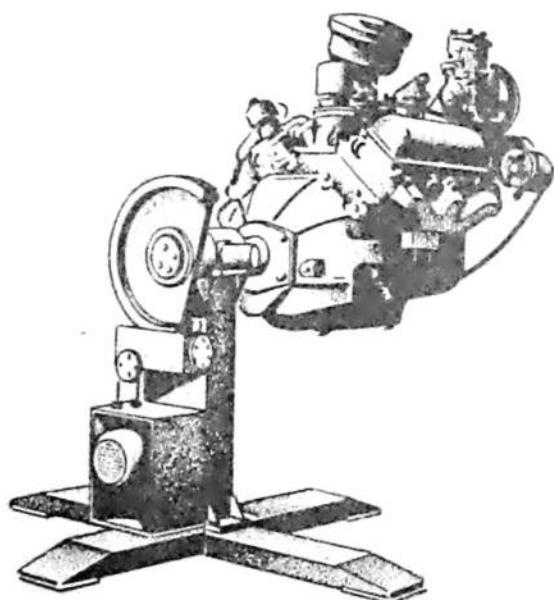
Стенд ОПТ-5557-ГОСНИТИ для разборки и сборки двигателей
